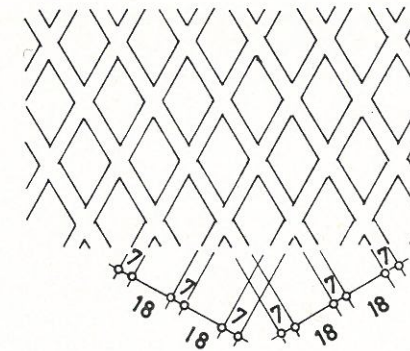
Aufsicht auf eine 3 mm starke Lochblechplatte.
